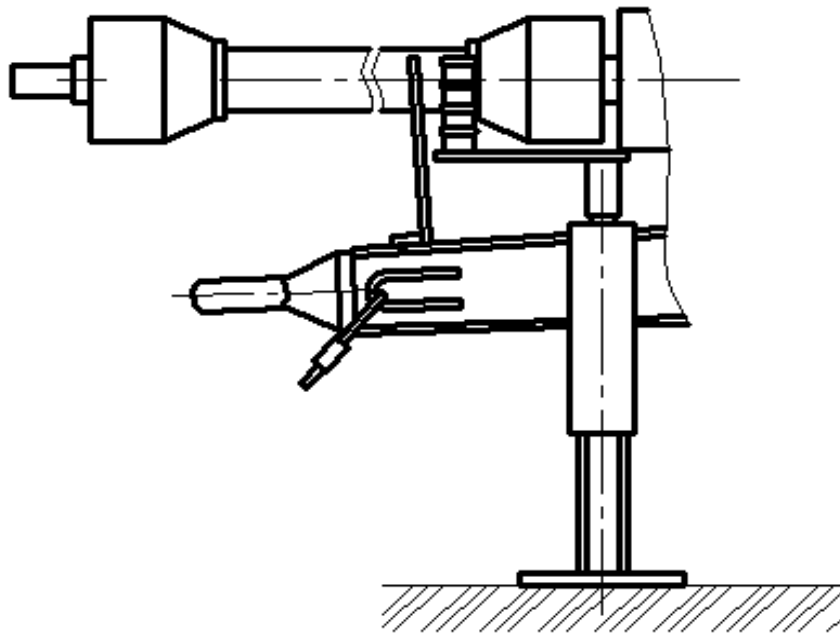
Установка стойки под карданный вал и установка опоры в рабочее положение
